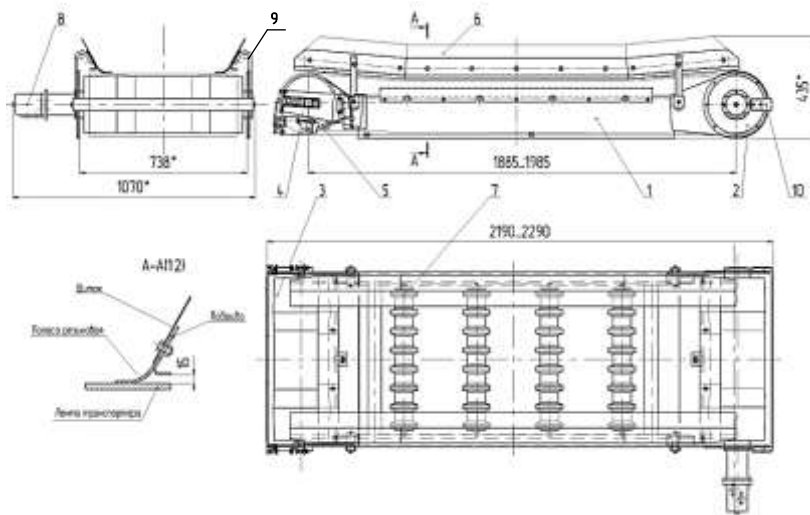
Транспортер: 1 – рама; 2 – ведущий барабан; 3 – натяжной барабан; 4 – механизм натяжения; 5 – лента; 6 – щиток; 7 – ролик; 8 – привод транспортера; 9 – кронштейн; 10 – грязесъемник
